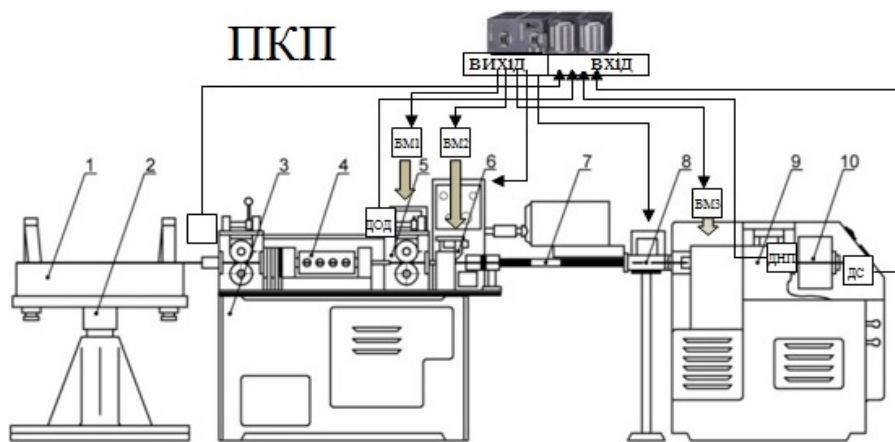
Агрегатно-модульний комплекс поперечно-клинової прокатки
